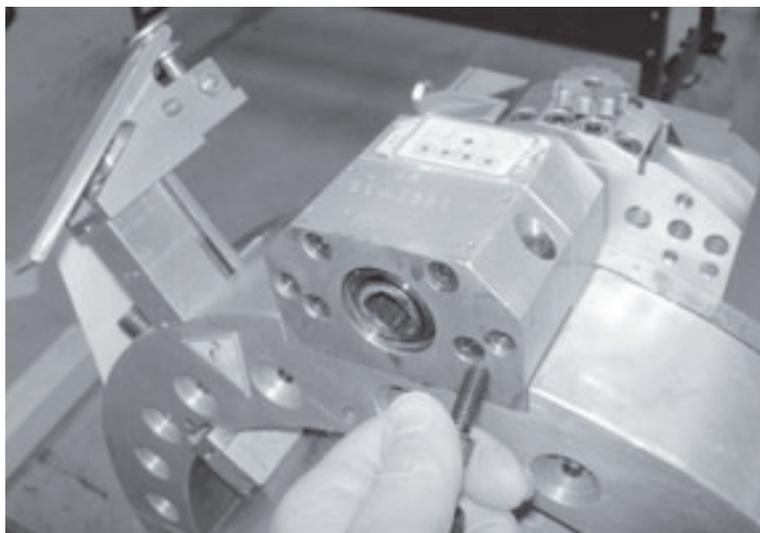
Rimuovere le viti di montaggio motore alla sede pignone e metterle da parte.
